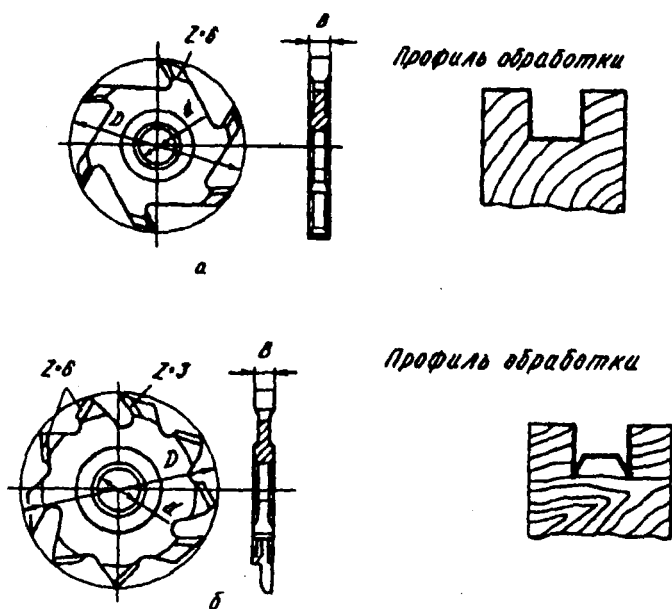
Фрезы для фрезерования пазов: а – для продольных пазов; б – для поперечных пазов с подрезающими зубьями
